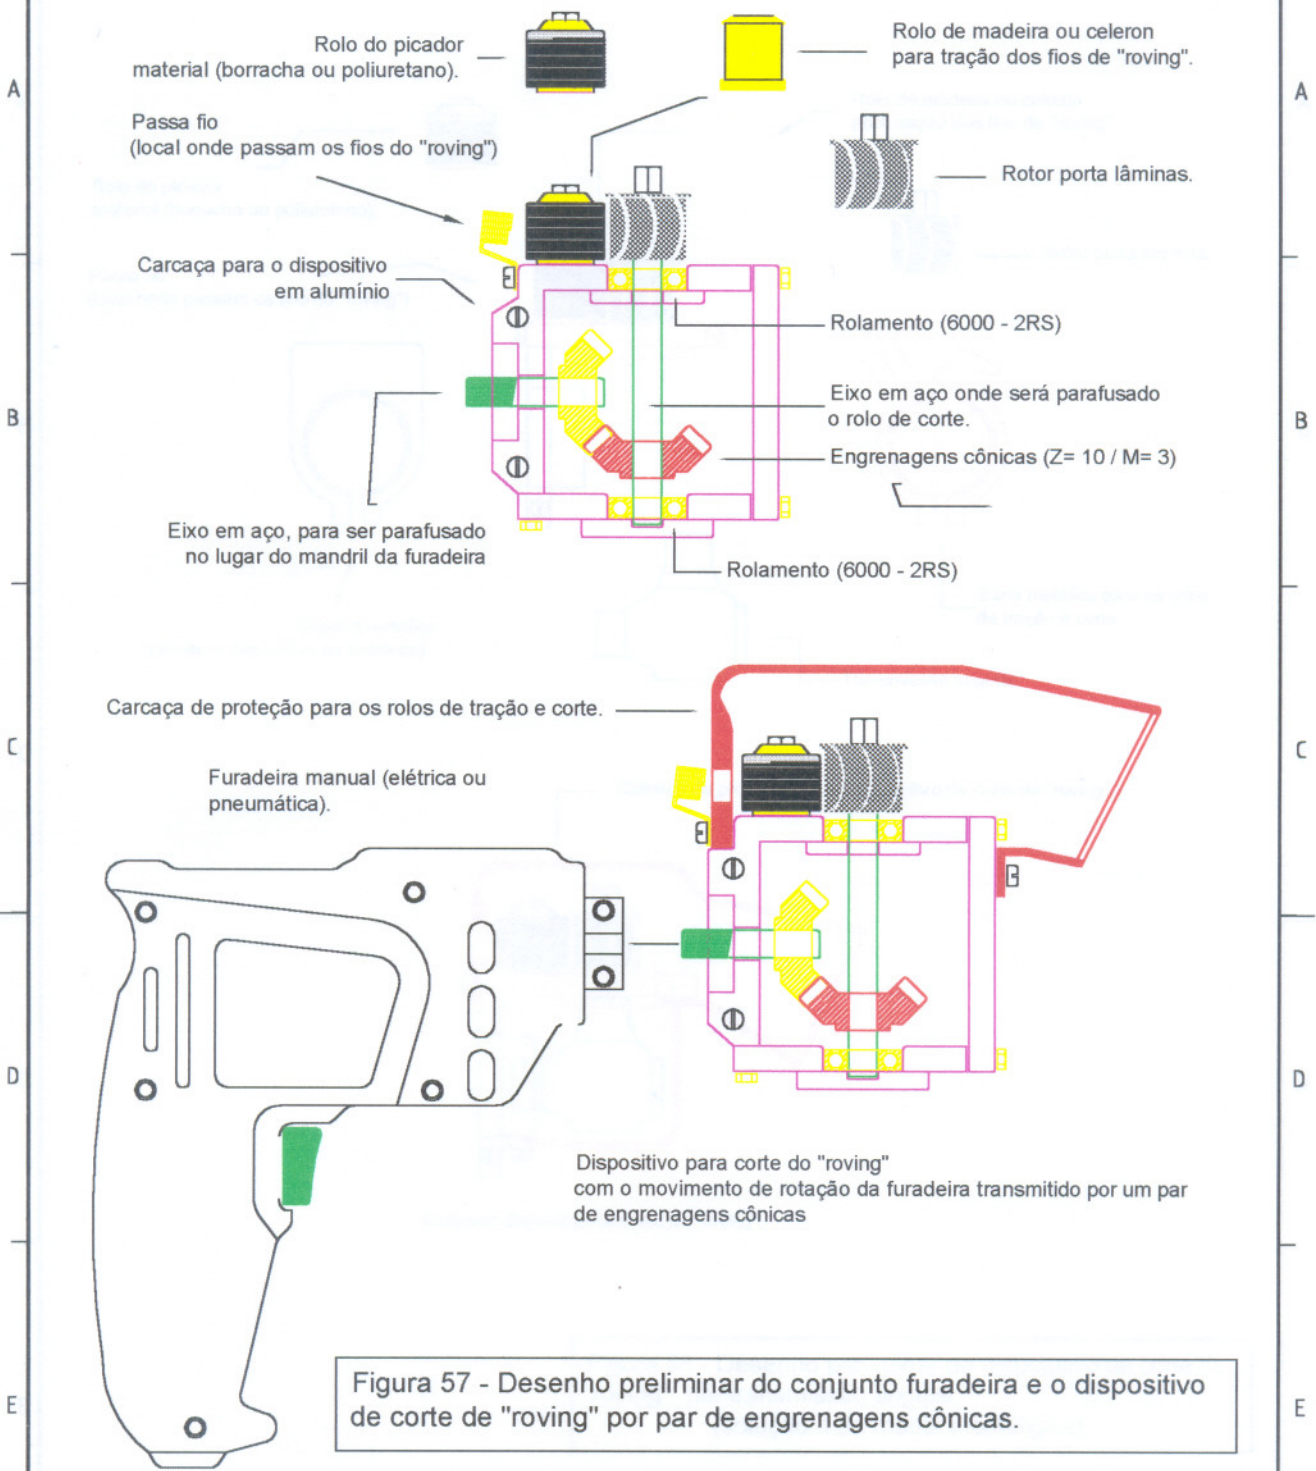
Desenho preliminar do conjunto furadeira e o dispositivo de corte de "roving" por par de engrenagens cônicas.
